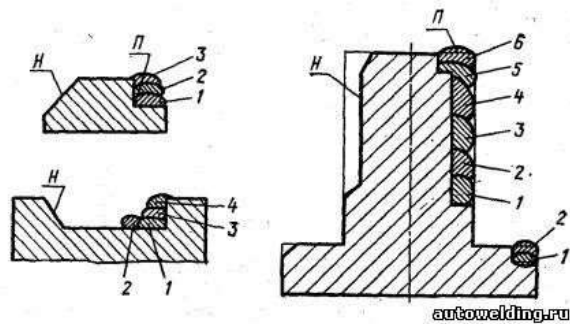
Правильная (П) рис.2а и неправильная (Н) рис.2б подготовка поверхностей под наплавку; 1...6 — последовательность наложения валиков рис.2в
